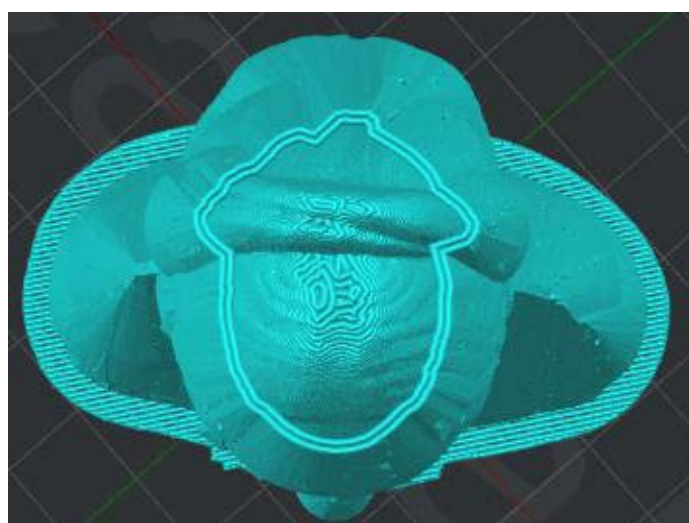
Nastavení úhlu Wipe Wall na 0.
